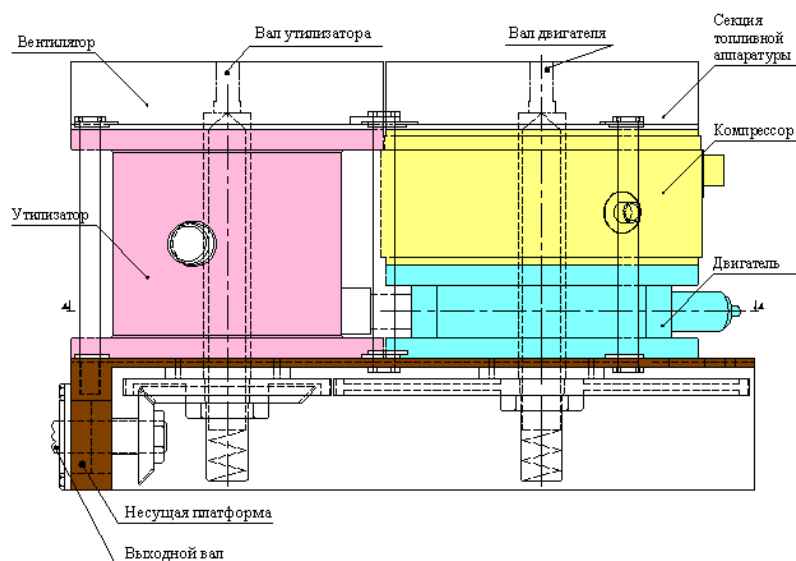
Общий вид и принципиальное устройство ДВС «Горник-2В» (пилотный образец)
